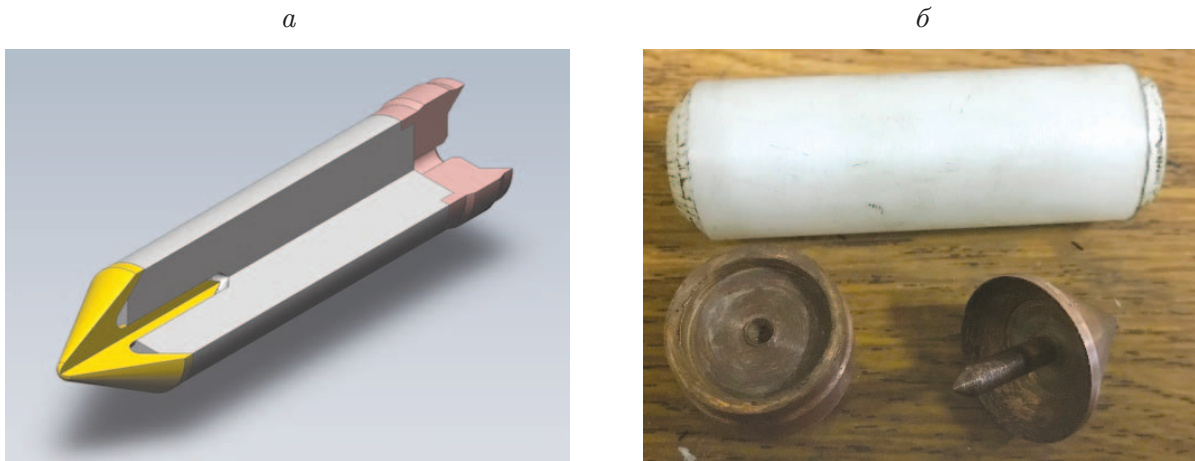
Конструкция (а) и общий вид (б) метаемой сборки
